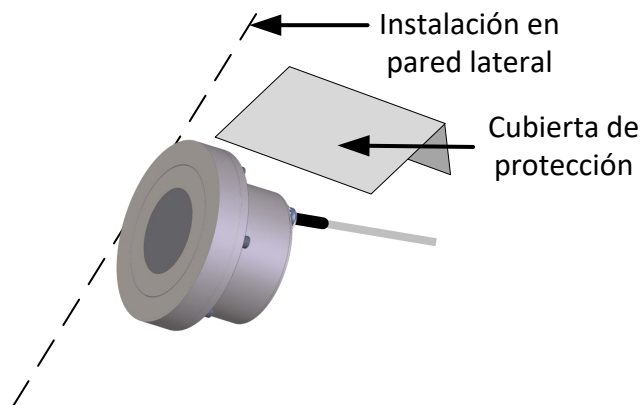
Hydro-Mix XT con cubierta de protección instalada
